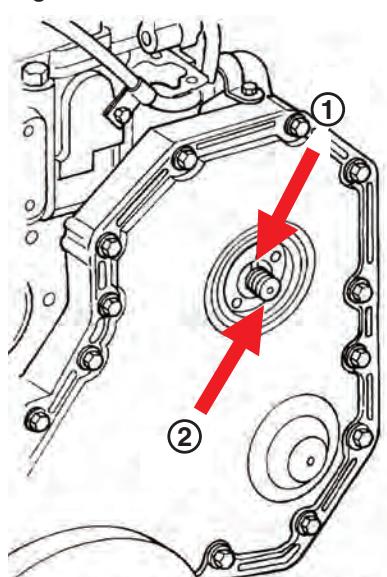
Colocar el chavetero en la posición de las 12 en punto
